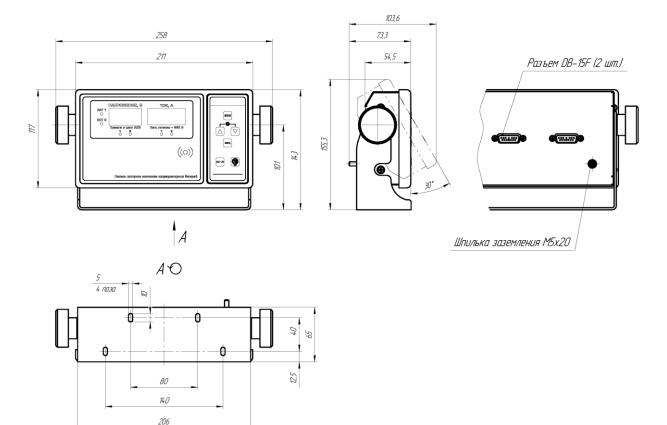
Габаритные и установочные размеры ПКБ-136, ПКБ-136-01
